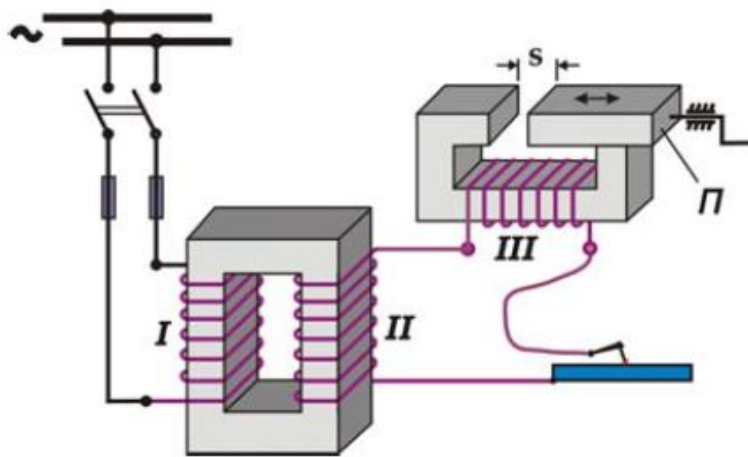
Схема сварочного трансформатора типа СТЭ 34
